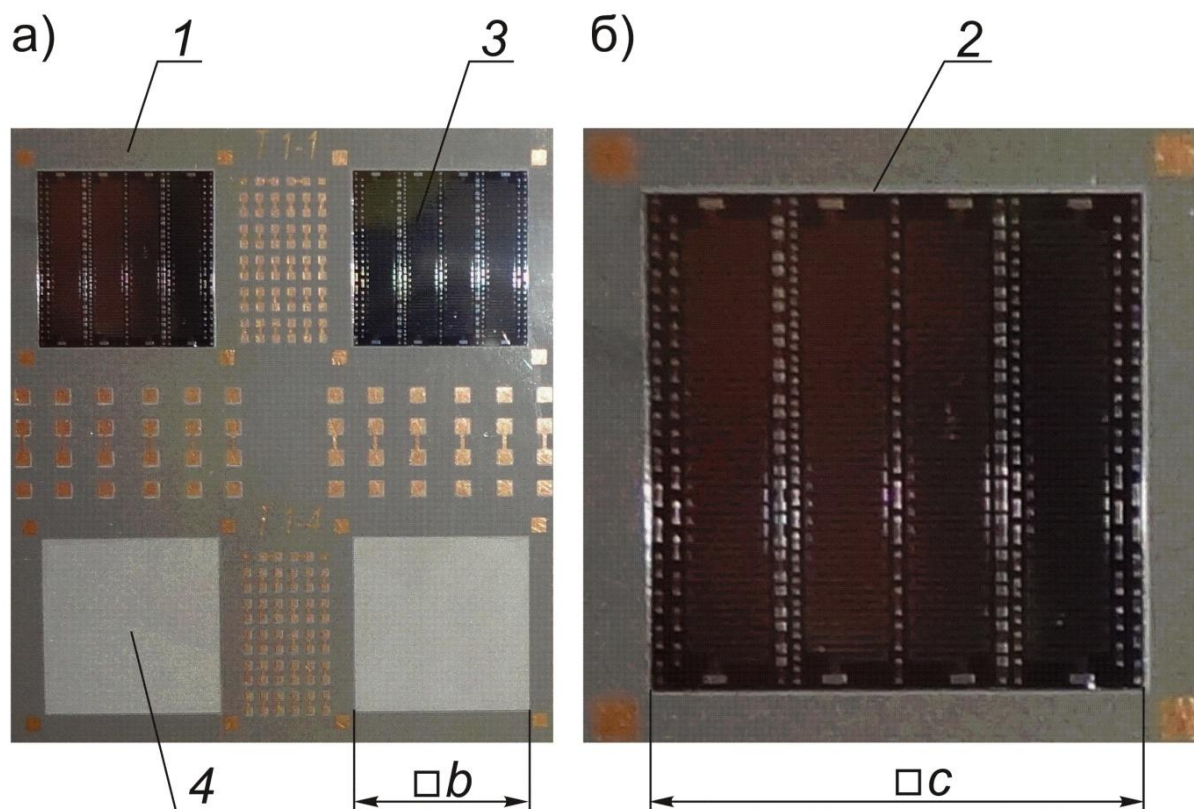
Образец тестовой платы с смонтированными кристаллами ИС на подложку в «окна» фотополимера SU-8; а) вид сверху на плату и б) вид сверху на кристалл (увеличено): 1 – конструкционный фотополимер SU-8, 2 – зазор между кристаллом и фотополимером, 3 – кристалл, 4 – подложка из нитрида алюминия. Изображение получено при помощи цифрового USB-микроскопа с максимальным увеличением 250х
